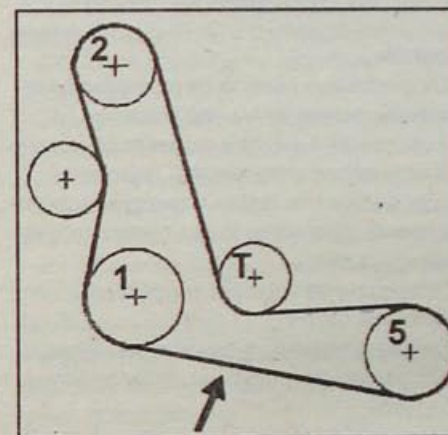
Расположение на шкивах ремня привода вспомогательного оборудования двигателя Z:
